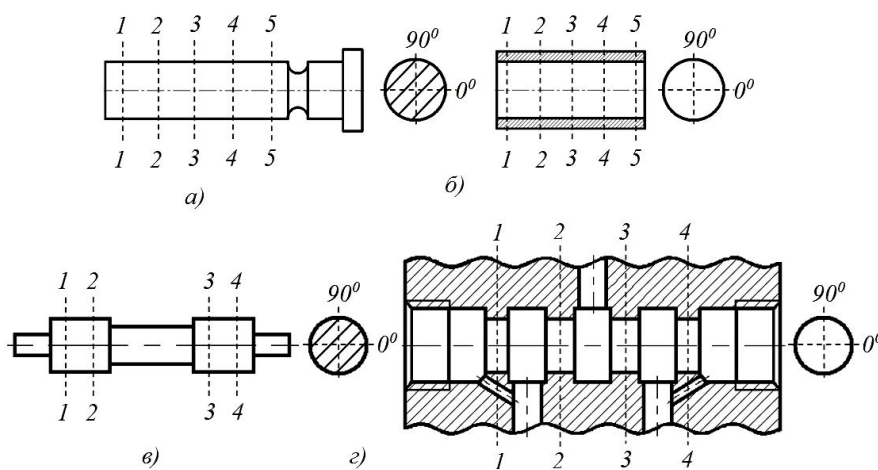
Схема измерения: а) – поршня; б) – втулка блока цилиндров; в) - золотника; г) – отверстия корпуса клапанной коробки
